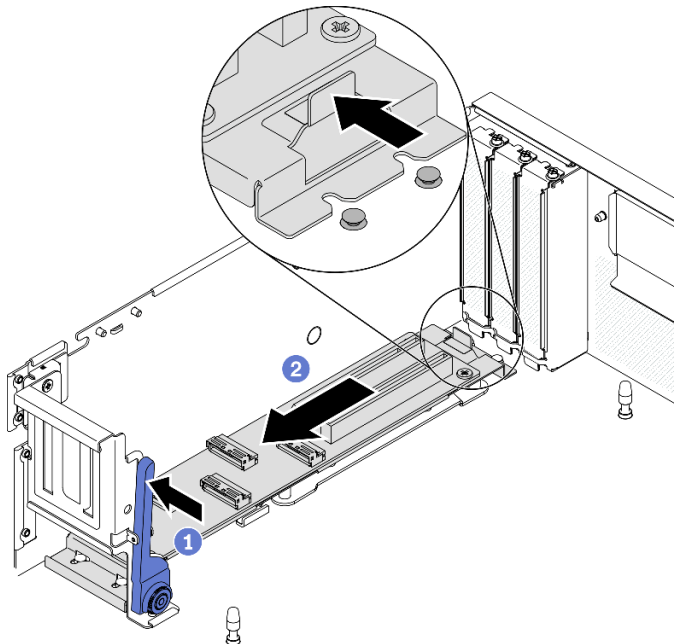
Desencaixando o módulo de placa de expansão de E/S frontal
